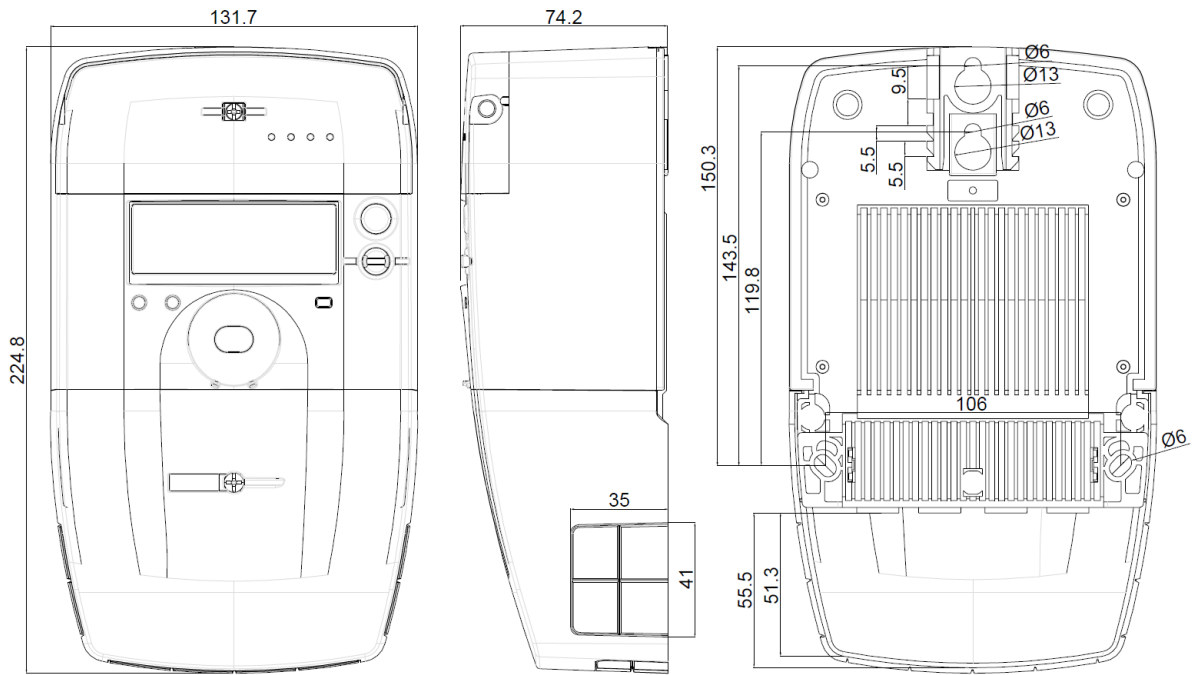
Габаритные и присоединительные размеры счетчика
